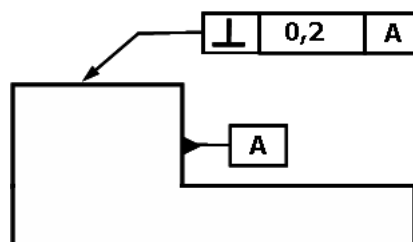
Indicação de tolerância de perpendicularidade em desenho técnico
